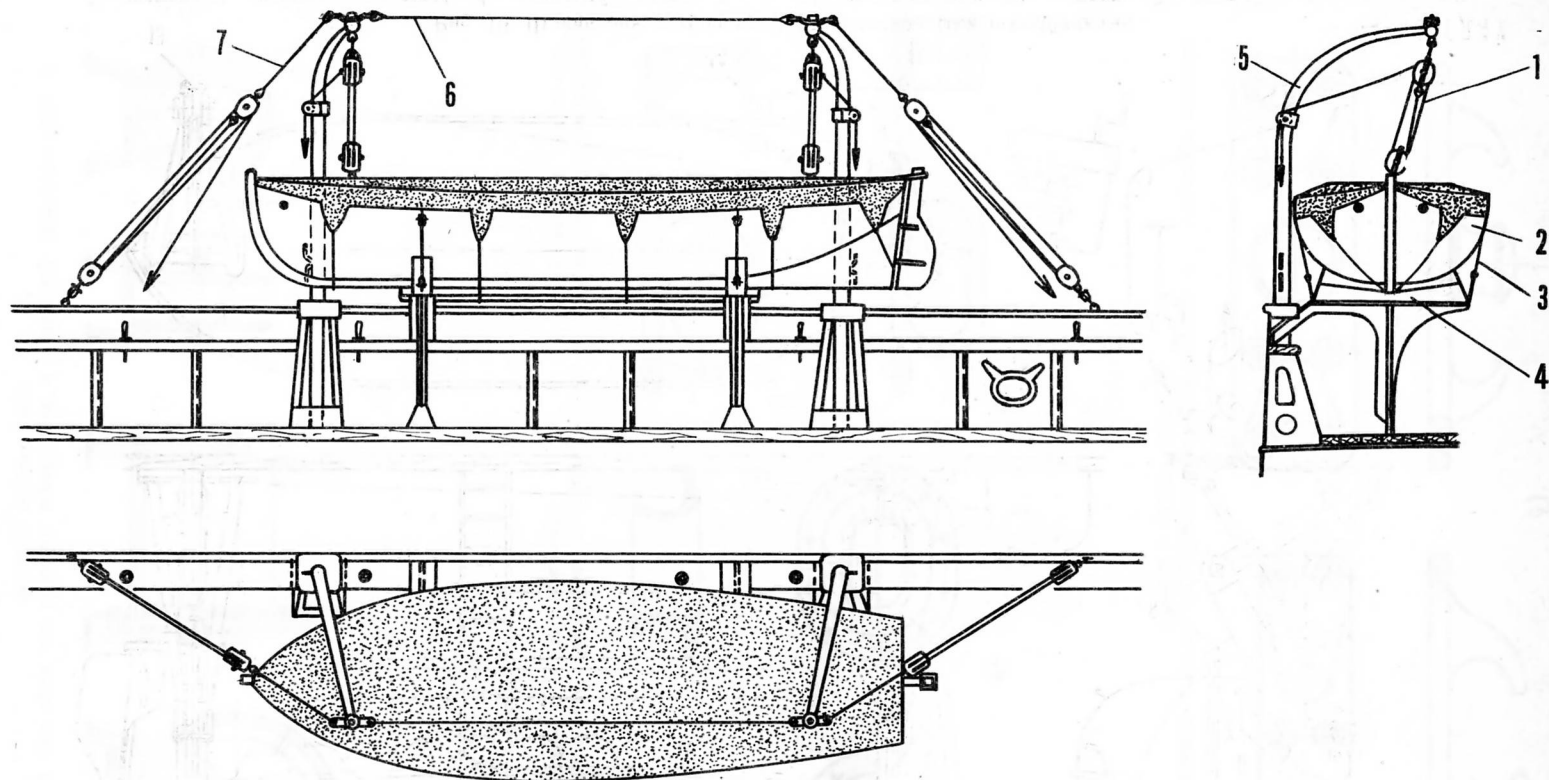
Шлюпочное устройство с поворотными шлюпбалками
